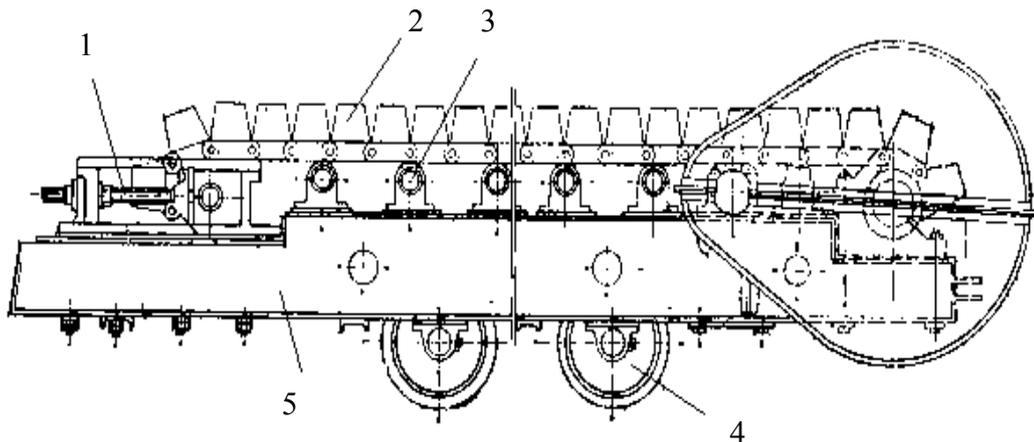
Пластинчатый конвейер-питатель: 1 – натяжное устройство; 2 – цепь с пластинами; 3, 4 – опоры; 5 – рама
